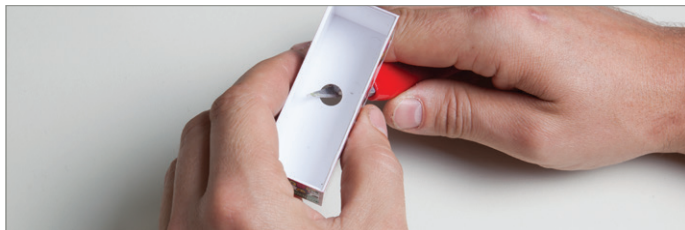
Bohrung im Fahrzeugaufbau ausbessern
